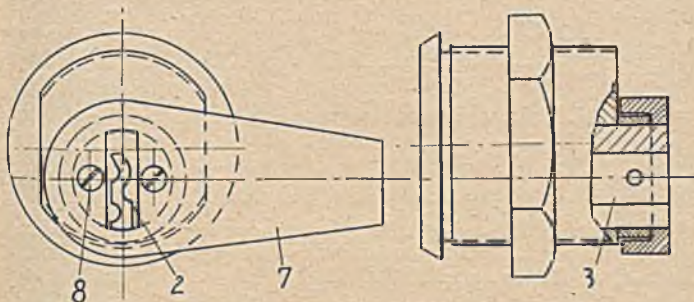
Schließnasenbefestigung mit Zweikant und Schrauben
